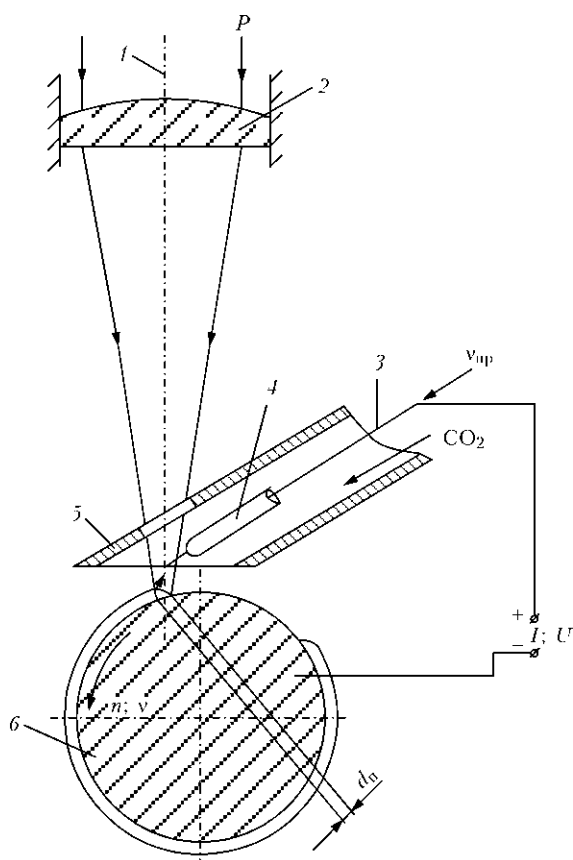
Схема процесса гибридной наплавки тел вращения: 1 — лазерное излучение; 2 — фокусирующая линза; 3 — электродная (присадочная) проволока; 4 — медный мунштук; 5 — сопло для подачи защитного газа; 6 — образец; P — мощность излучения, кВт; $v_{пр}$ — скорость подачи присадочной проволоки, м/ч; n — частота вращения образца, мин⁻¹; v — скорость наплавки, м/ч; $d_{л}$ — диаметр пятна фокусирования излучения, мм; I — сварочный ток, А; U — напряжение, В
